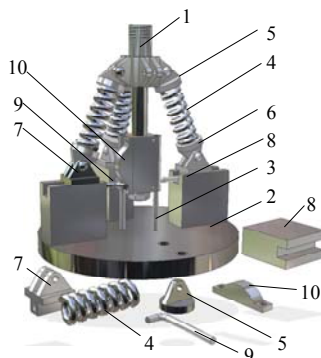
Виброизолирующее устройство с цилиндрическими витыми пружинами
